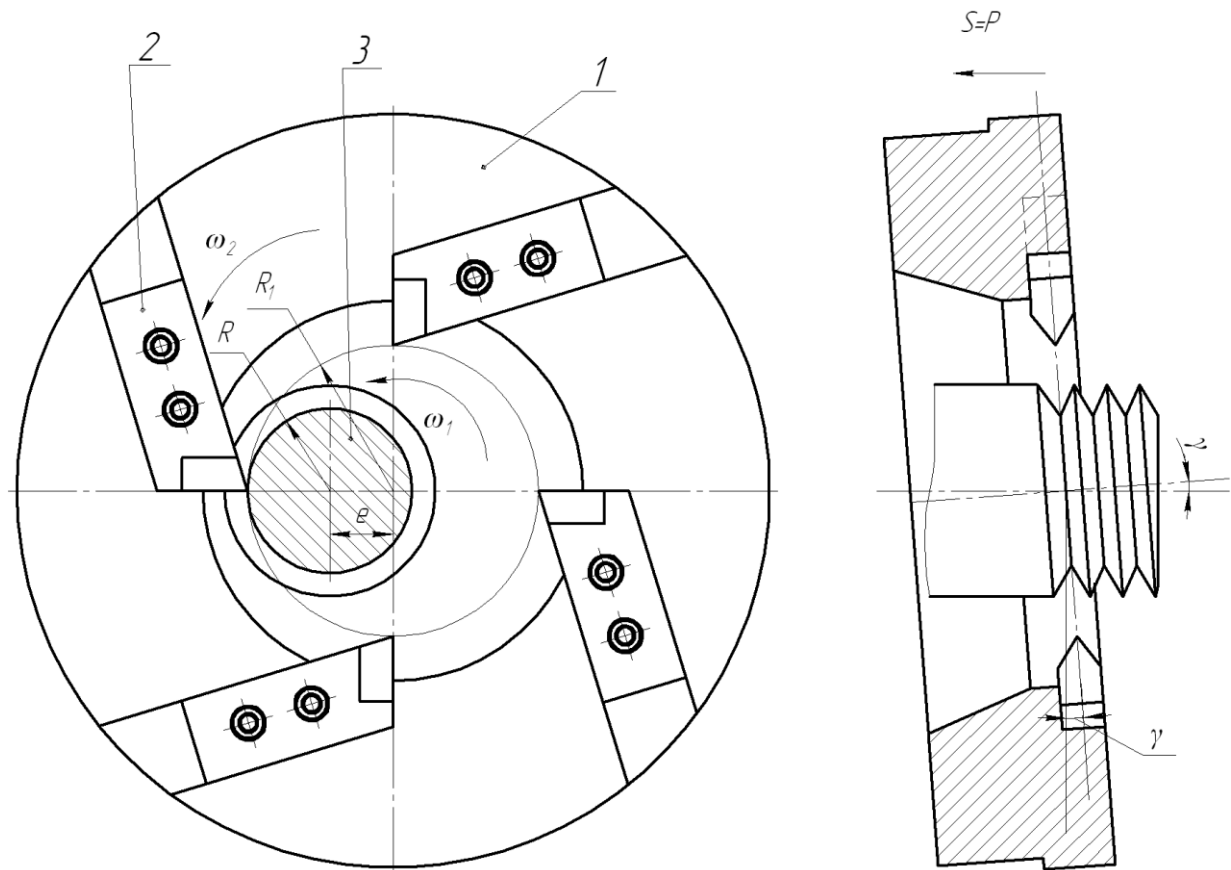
Конструкція спеціального багаторізевого інструменту для нарізання зовнішньої гвинтової поверхні: 1 – корпус, 2 – різець, 3 - заготовка
